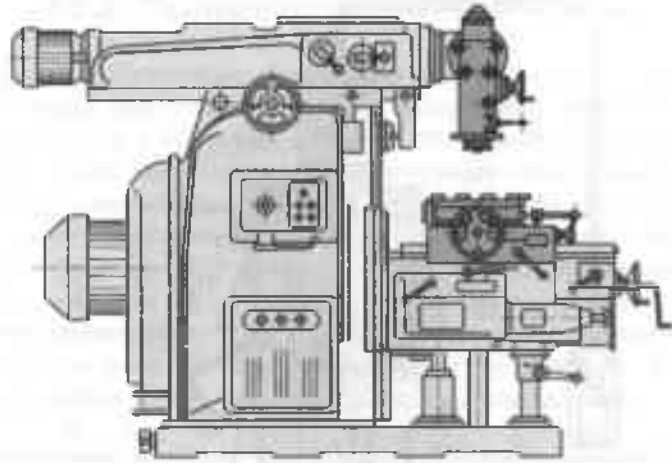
Широкоуниверсальный фрезерный станок модели 6M83Ш
